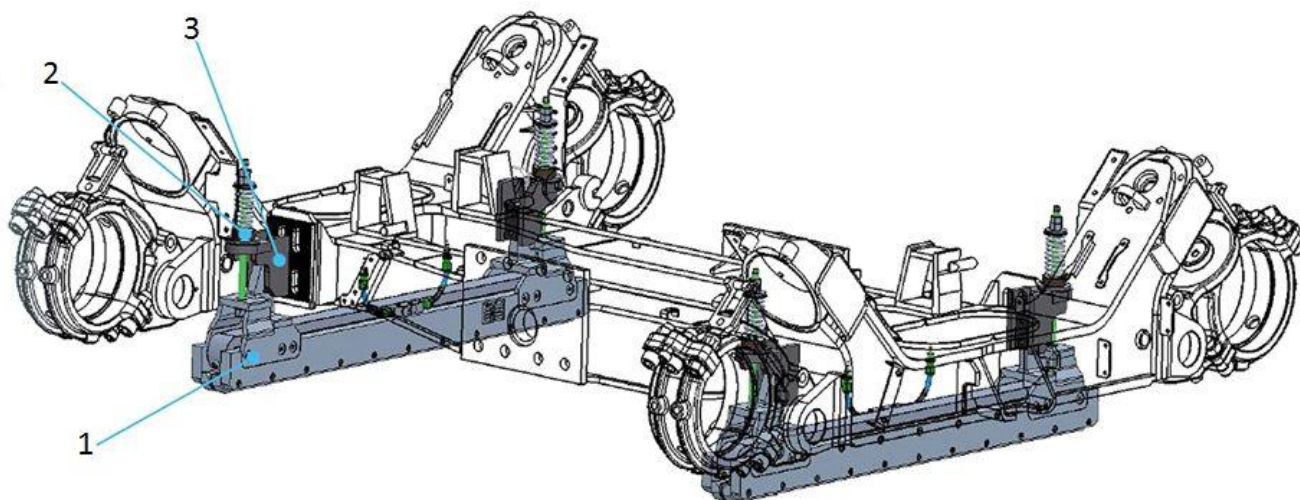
Установка и крепление рельсового тормоза на тележке:
